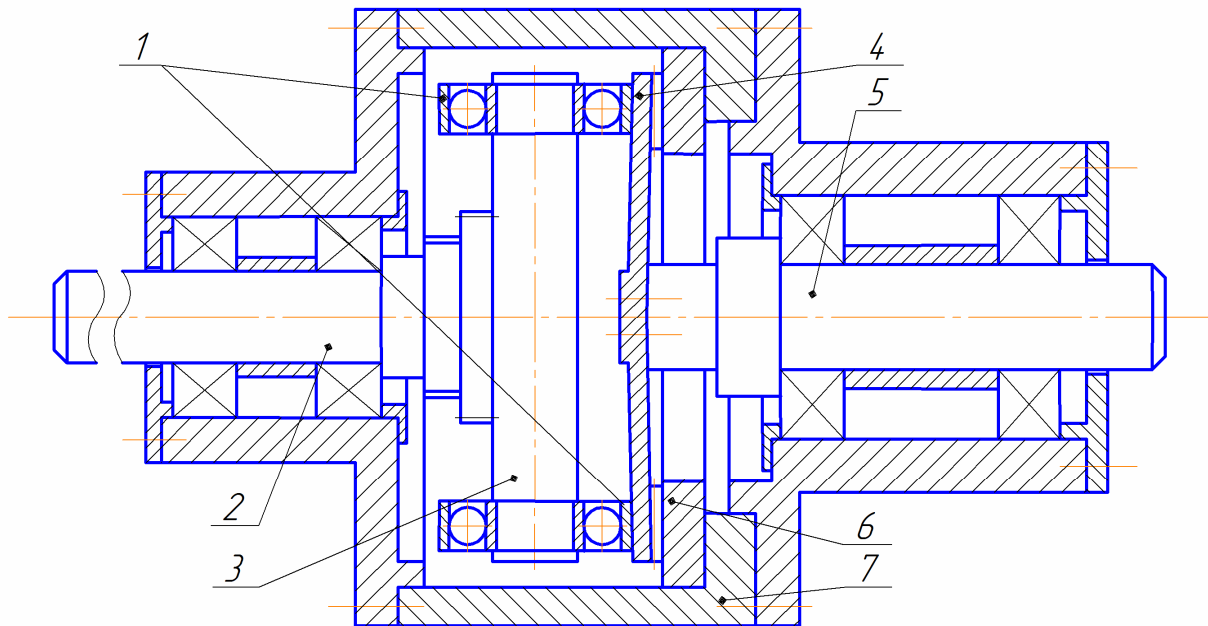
Конструктивная схема волновой торцевой зубчатой передачи: 1 - подшипники, 2 - входной вал, 3 - генератор волн, 4 - гибкое колесо, 5 - выходной вал, 6 - жесткое колесо, 7 – корпус с крышками
